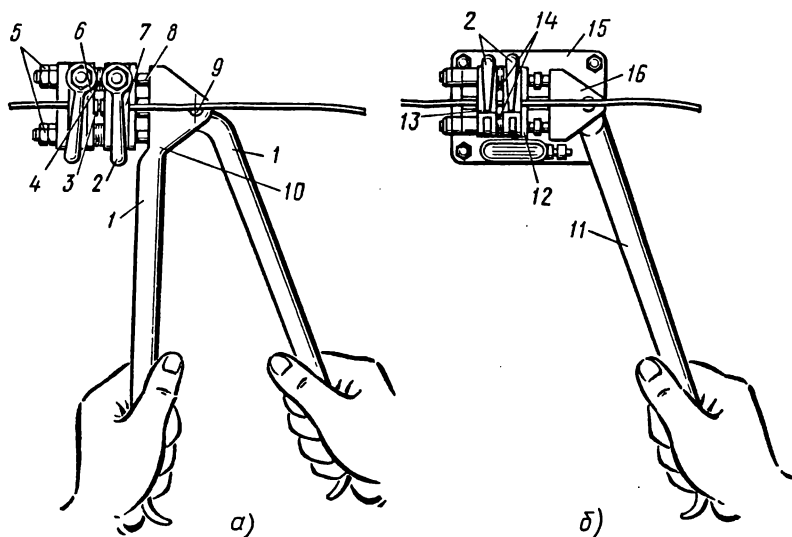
Ручные сварочные клещи КС-6 (а) и настольный сварочный станок СНС-3 (б):
